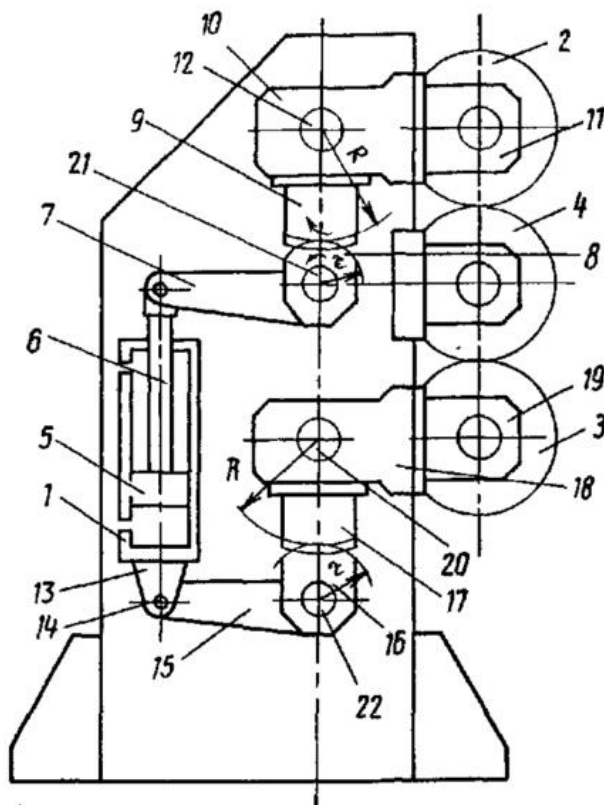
Загальний вигляд пристрою для притискання валків
